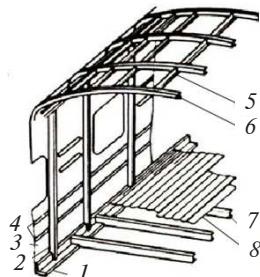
Каркас кузова вагона без хребтовой балки:
